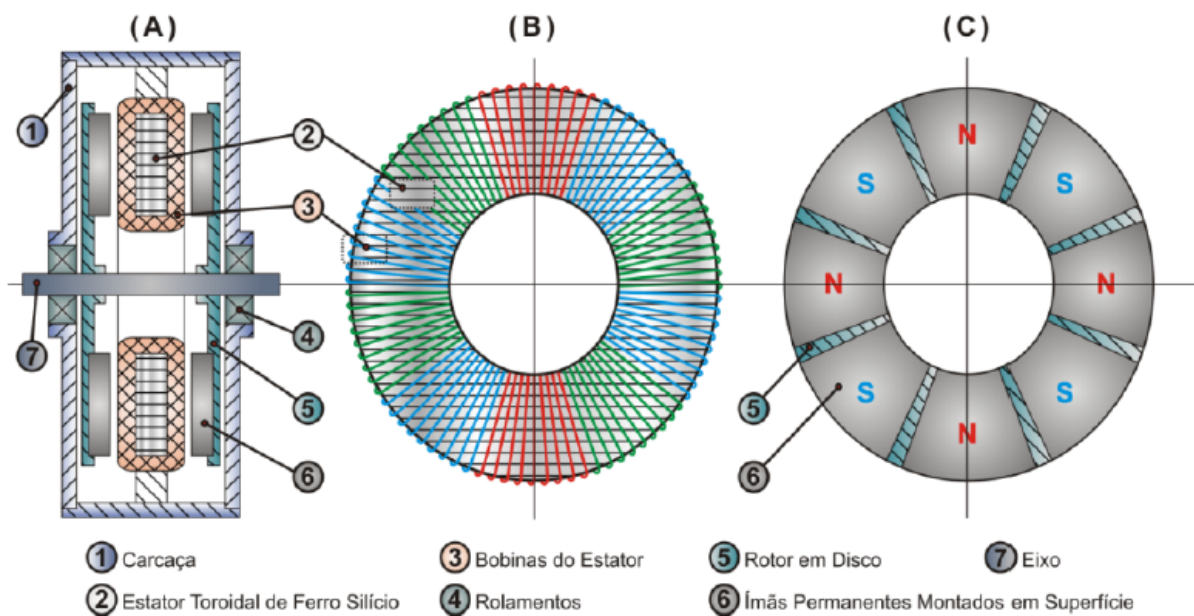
Vista externa de um PMSG com fluxo axial (máquina Torus). (a) Estrutura construtiva; (b) Vista frontal do estator com seus enrolamentos; (c) Vista frontal do disco de ímãs [10].
